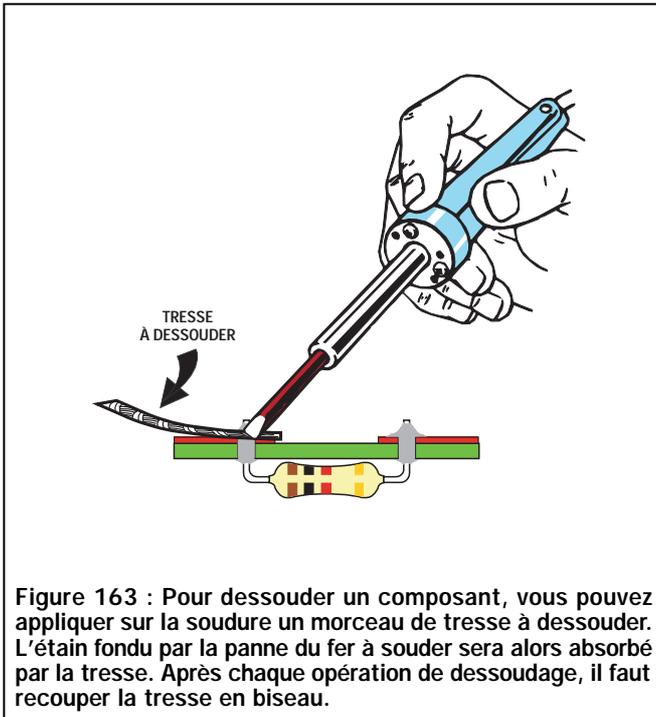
Pour dessolder un composant, vous pouvez appliquer sur la soudure un morceau de tresse à dessouder. L'étain fondu par la panne du fer à souder sera alors absorbé par la tresse. Après chaque opération de dessoudage, il faut recouper la tresse en biseau.
